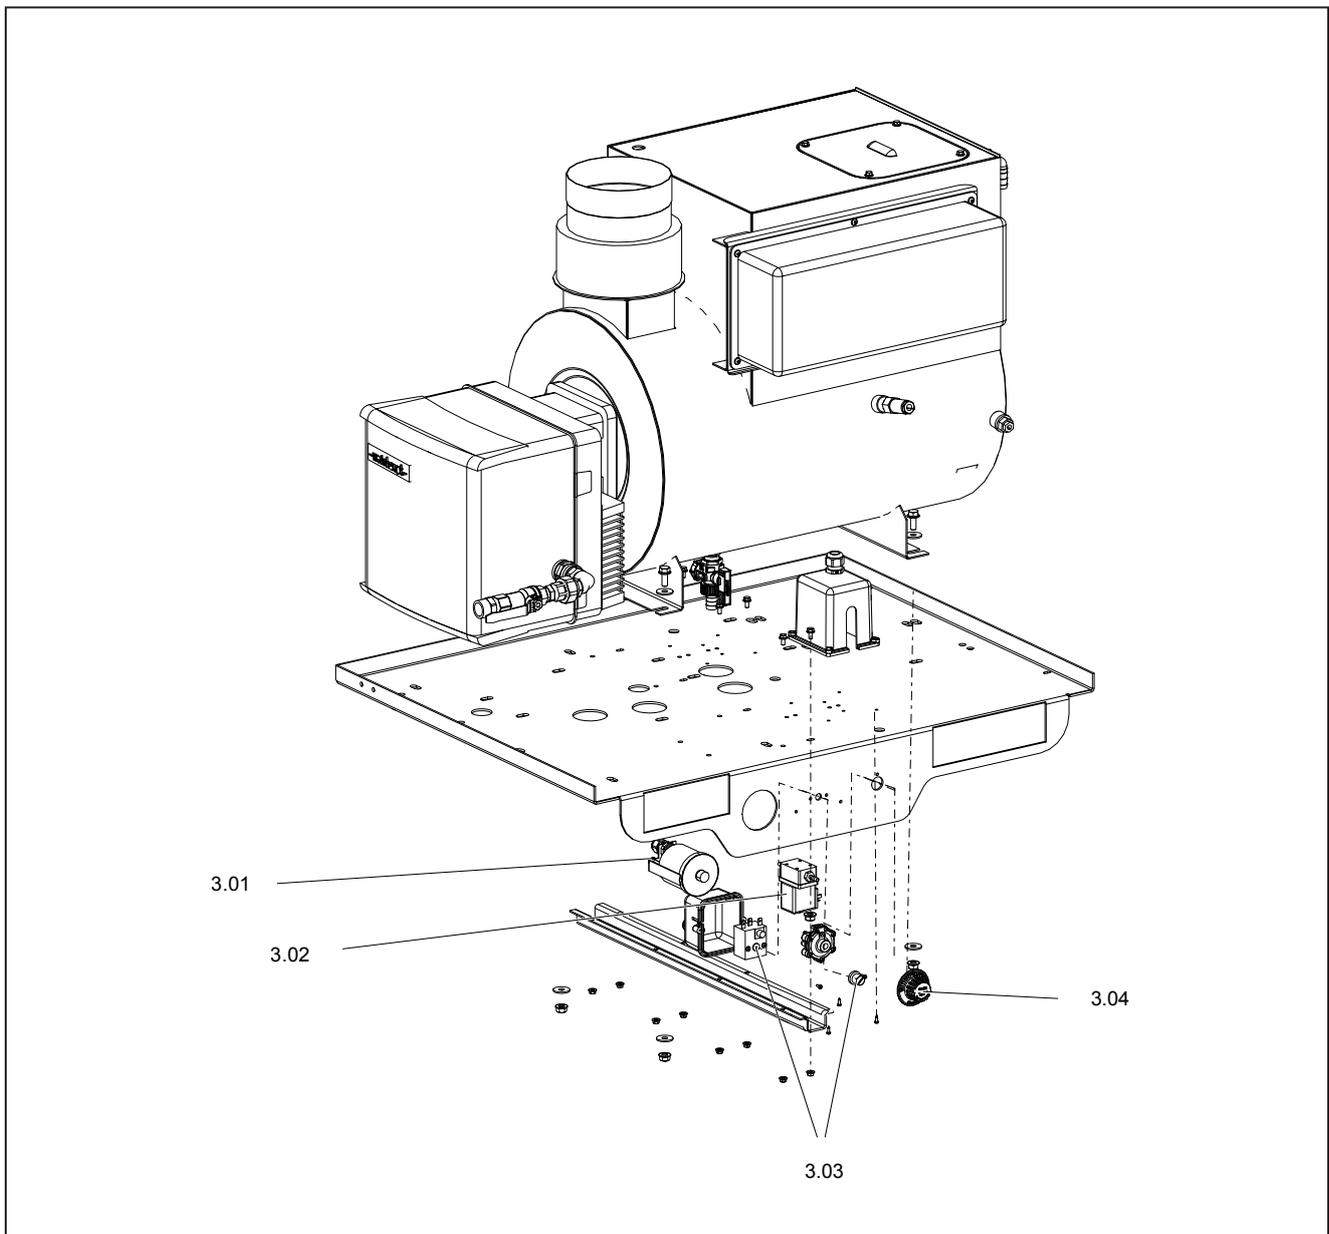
3 Komponenten am Chassis-Mittelteil, Explosionszeichnung
